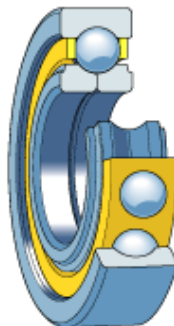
Ángulo de contacto en rodamientos de bolas con contacto angular.
